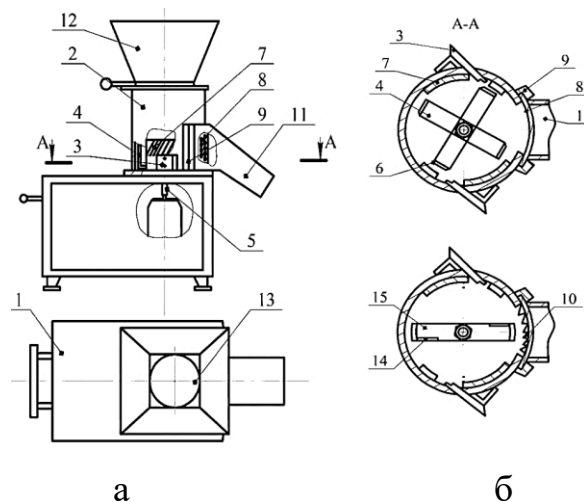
«Универсальный измельчитель кормов по патенту № 94042038: а – общий вид, б – вид А-А
